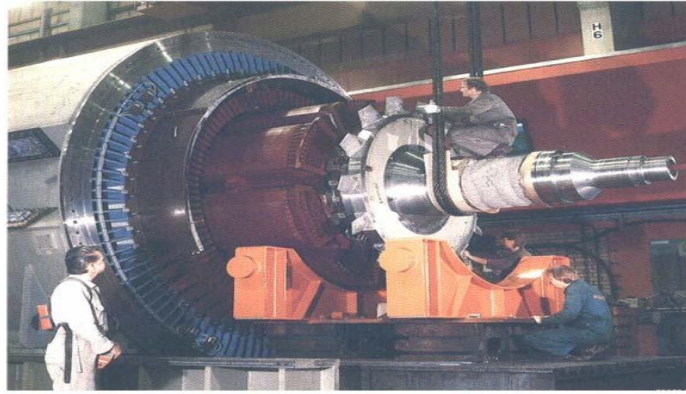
rotor d'une machine synchrone à pôles saillants.
